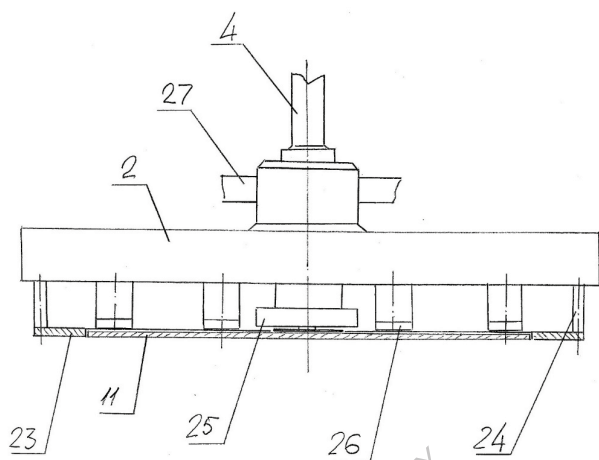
Схема нового вида захвата для полупроводниковой пластины
